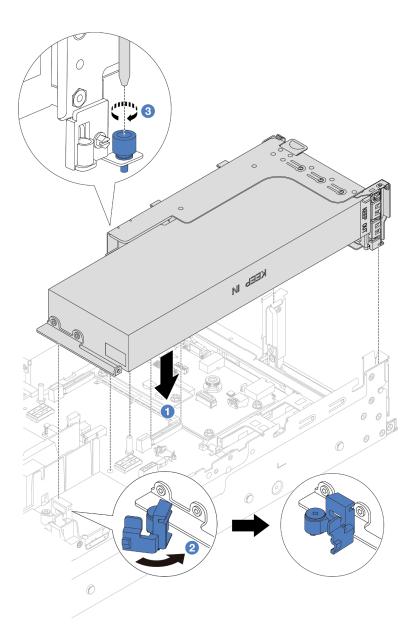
Установка блока платы-адаптера Riser 1 с адаптером графического процессора
